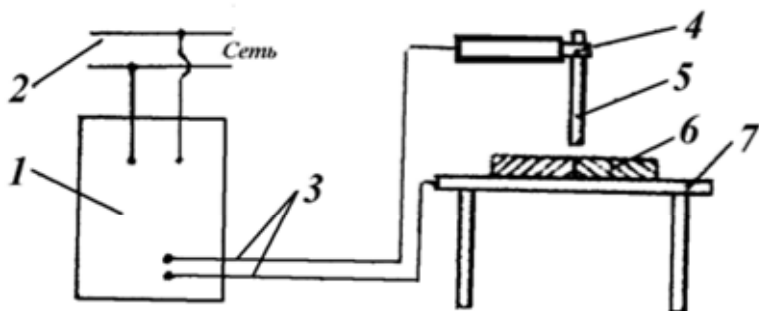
Схема сварочного поста для ручной дуговой сварки: 1 - источник сварочного тока; 2 — сеть переменного тока; сварочные провода (сварочная цепь); 4 - держатель; 5 - электрод; 6 - свариваемые детали; 7- стол
